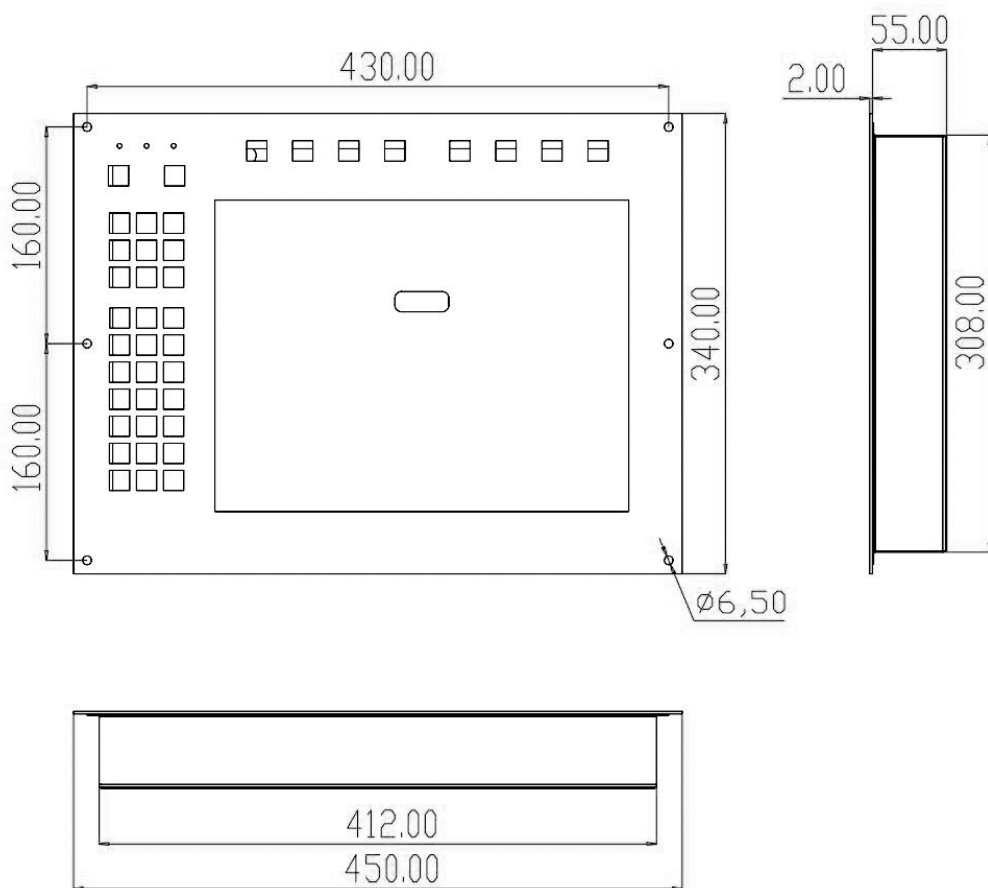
Установочные размеры ЧПУ контроллера FX450A.
